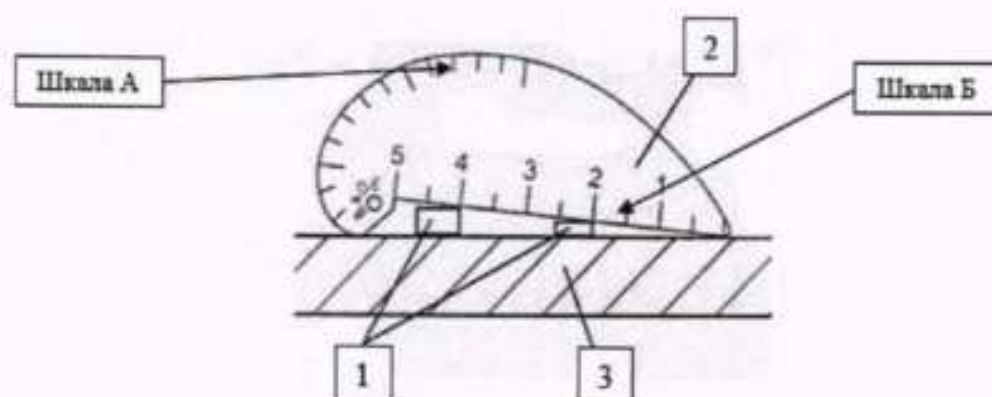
Схема размещения концевых мер длины при поверке шаблона;
